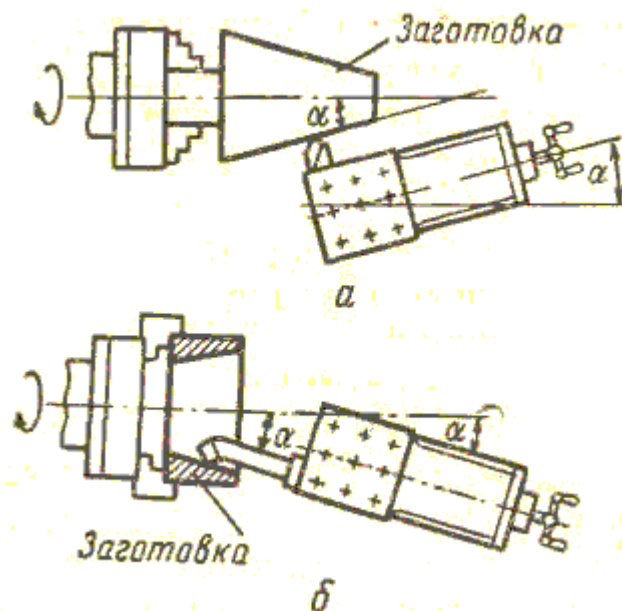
Обработка конической поверхности при повернутых верхних салазках суппорта
